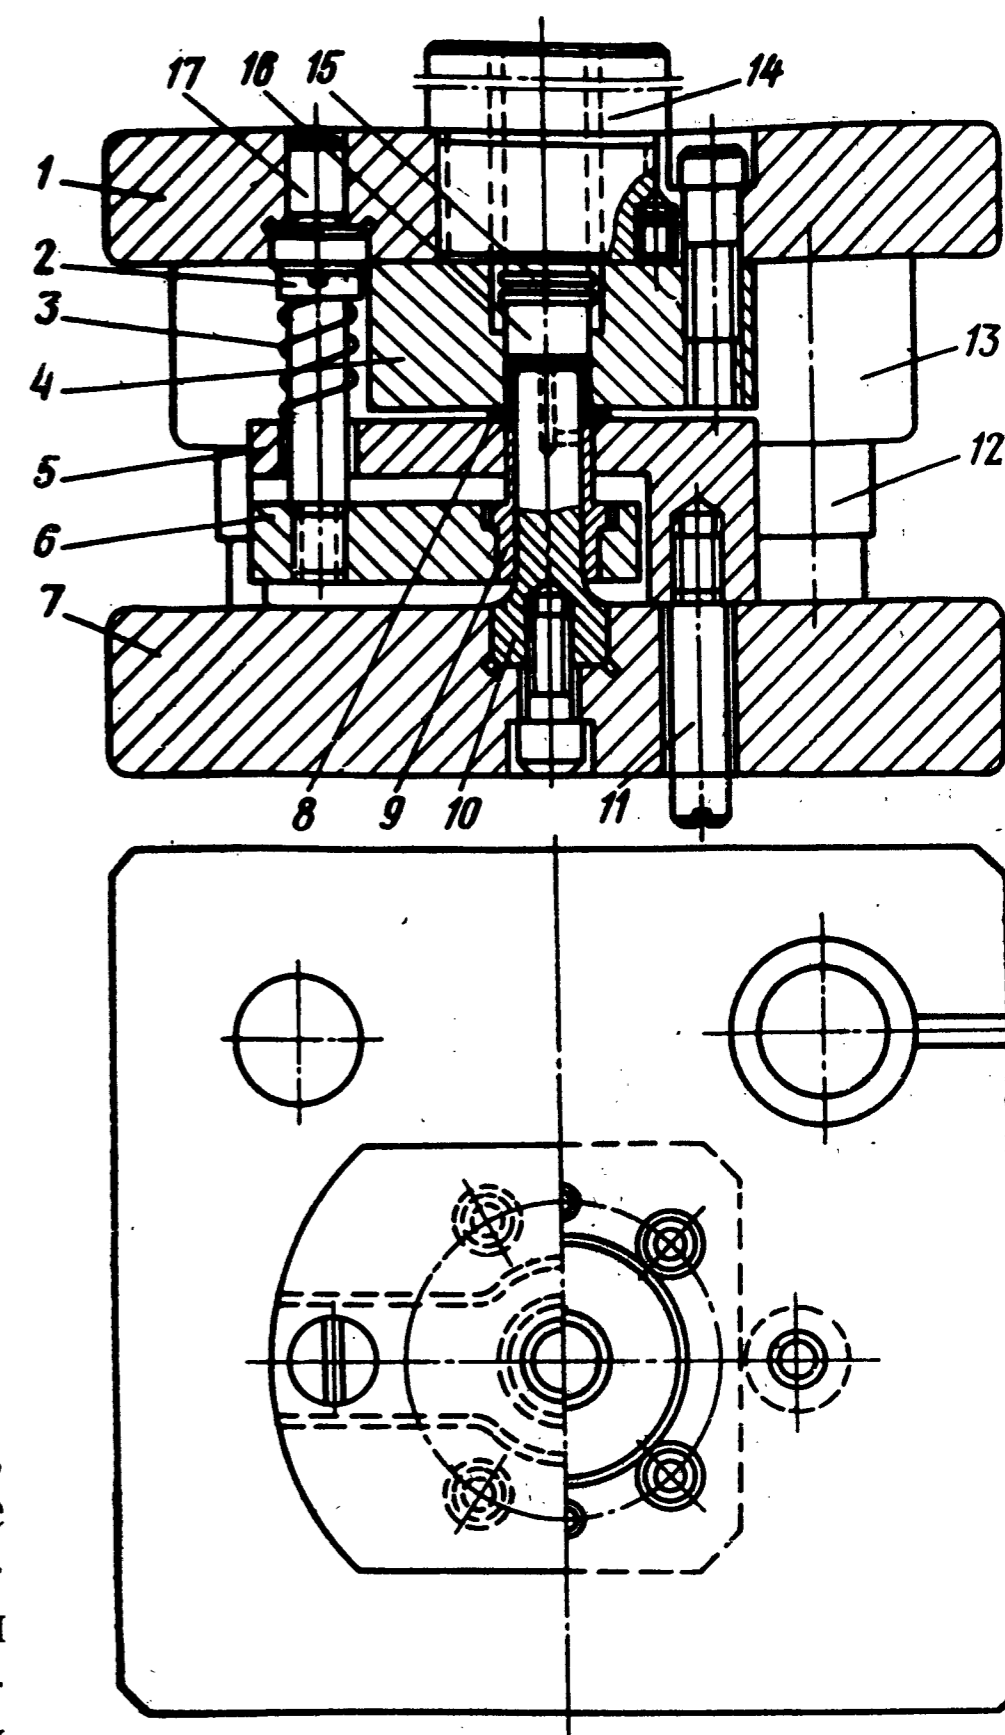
Штамп для повторной вытяжки тонкостенного цилиндра
